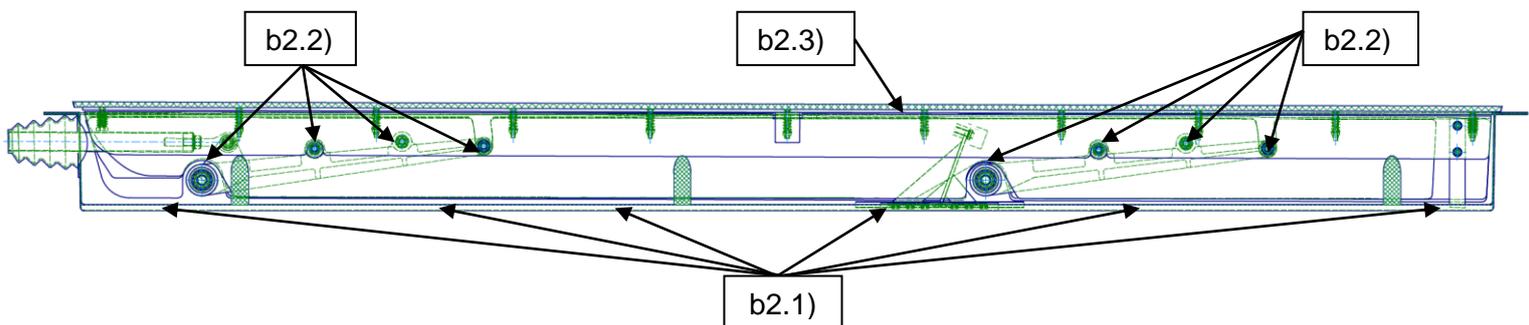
Schnitt durch Bremsklappenkasten bei eingefahrener Bremsklappe
